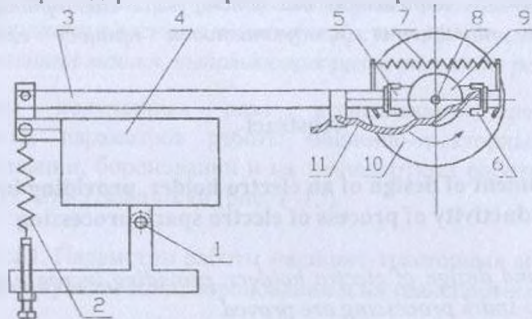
Конструкция электрододержателя, обеспечивающая повышение производительности процесса ЭИО: 1 - ось качения корпуса электрододержателя; 2, 7 - пружина; 3 - корпус вибратора; 4 - электромагнит вибратора; 5 - токоподводящие щетки; 6 - щеткодержатели; 8 - ось вращения электрода; 9 - коллектор; 10 - дисковый электрод; 11 - токопровод.
